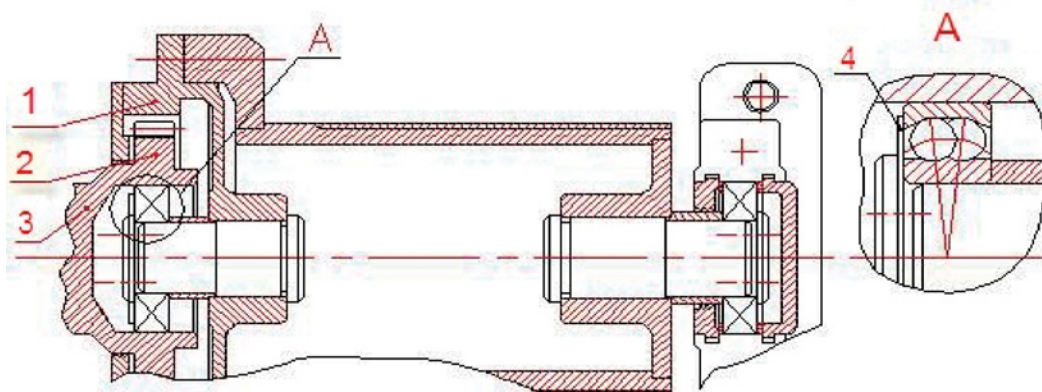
Конструкция соединения редуктора с барабаном при помощи зубчатой муфты со встроенной опорой в вал редуктора
